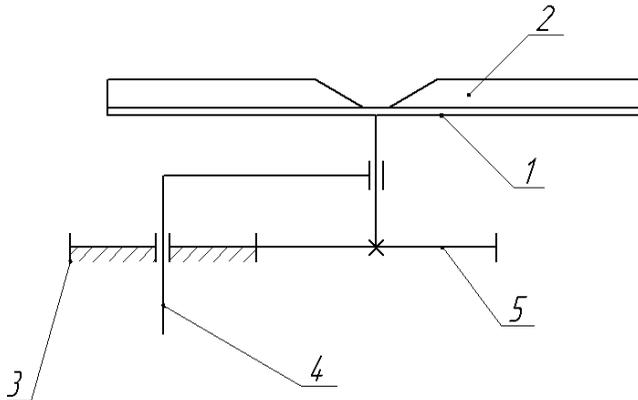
Кінематична схема планетарного приводу тукорозсівних апаратів: 1 – розкидний диск; 2 – лопатка; 3 – нерухома шестерня; 4 – вал гідро двигуна; 5 – шестерня
